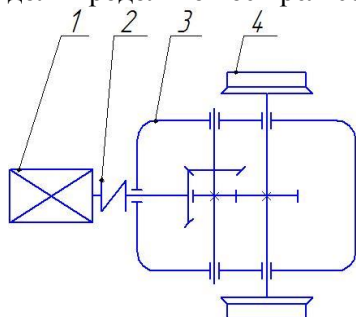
Стандартный приводной редуктор шахтного электровоза
